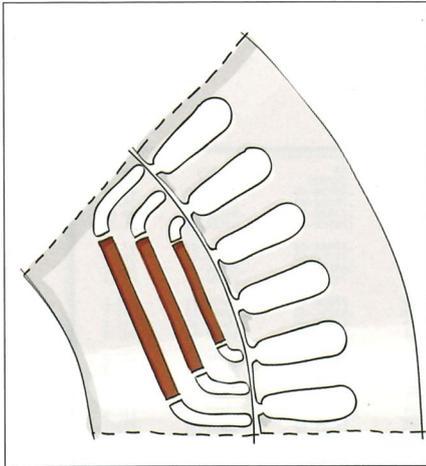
Beim IPM-Motor werden die Magnete im Rotor integriert bzw. im Rotorblechpaket eingebettet
